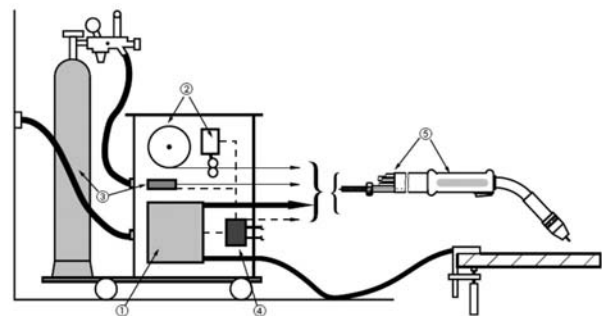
Funktionsprinzip des Schweißgeräts
